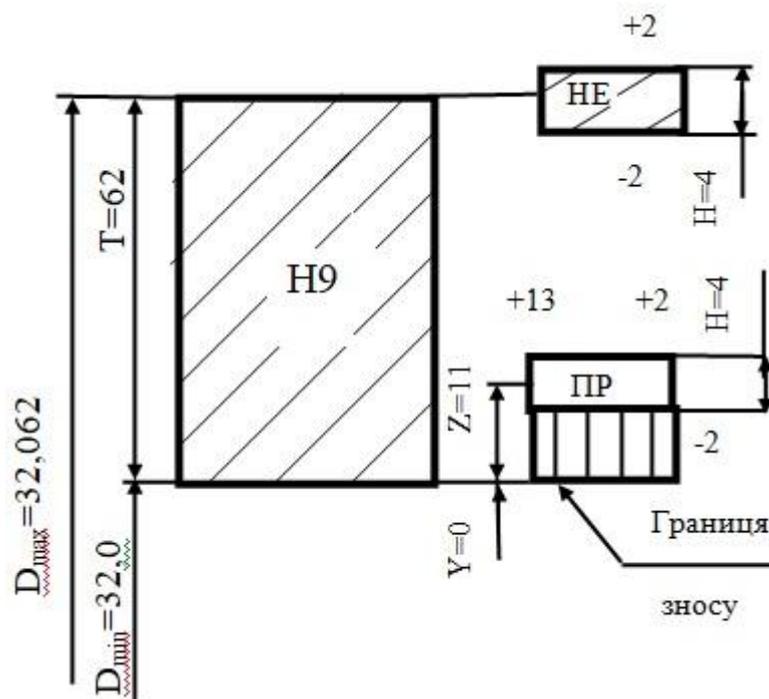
Схема розміщення полів допусків калібрів-пробок для контролю отвору $\varnothing 32H9(+0,062)$
